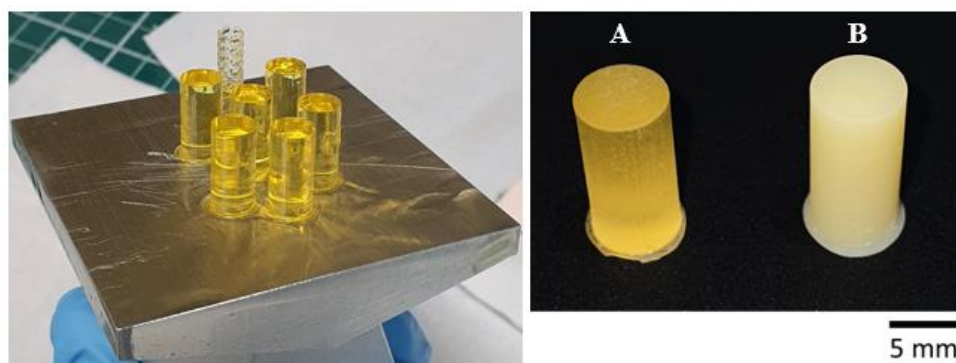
Corpos de prova de compressão de a) PCLMA e; b) PCLMA10S
